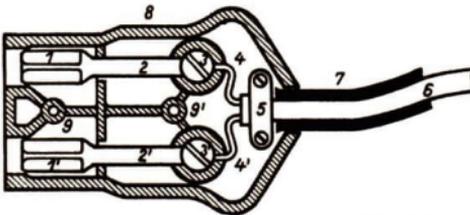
Gerätestecker (Deckel entfernt). 1,1' Metallhülsen; 2,2' Metallbänder; 3,3' Klemmschrauben; 4,4' Leitungsdrähte; 5 Befestigungsschelle; 6 Kabel; 7 Schutzhülle; 8 Gehäuse aus Isoliermasse; 9,9' Verbindungsschrauben
